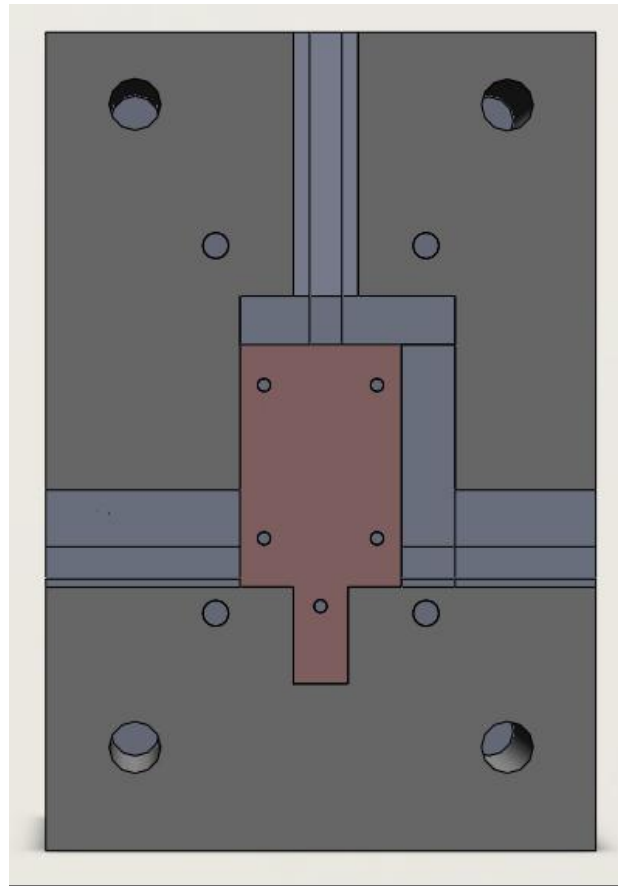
Vista en planta de la configuración de llenado central corto.
